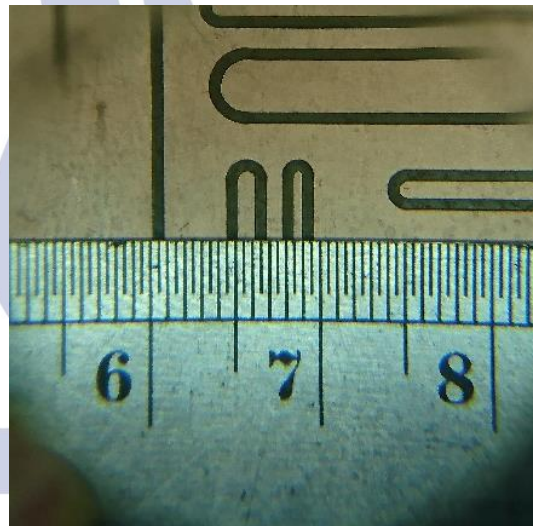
Hasil kecepatan milling pada 10 PCB pengujian
